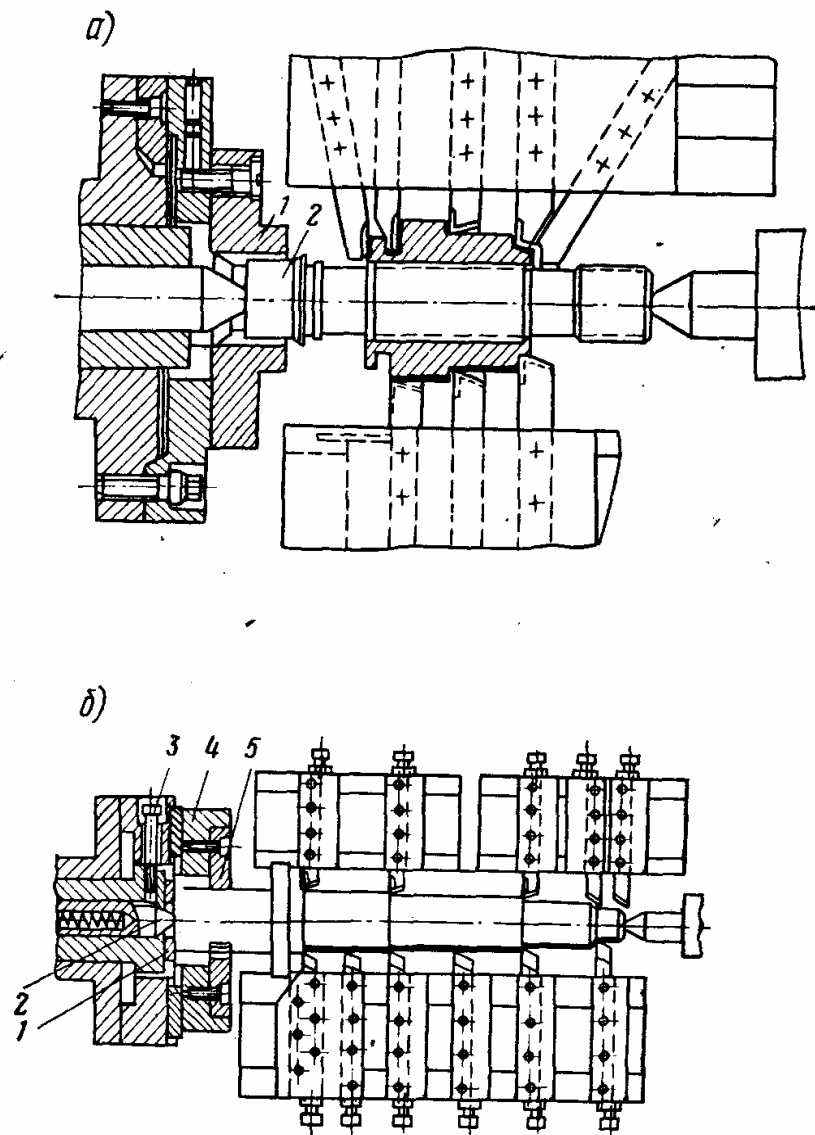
Схемы наладки многолезцового станка для обтачивания:
